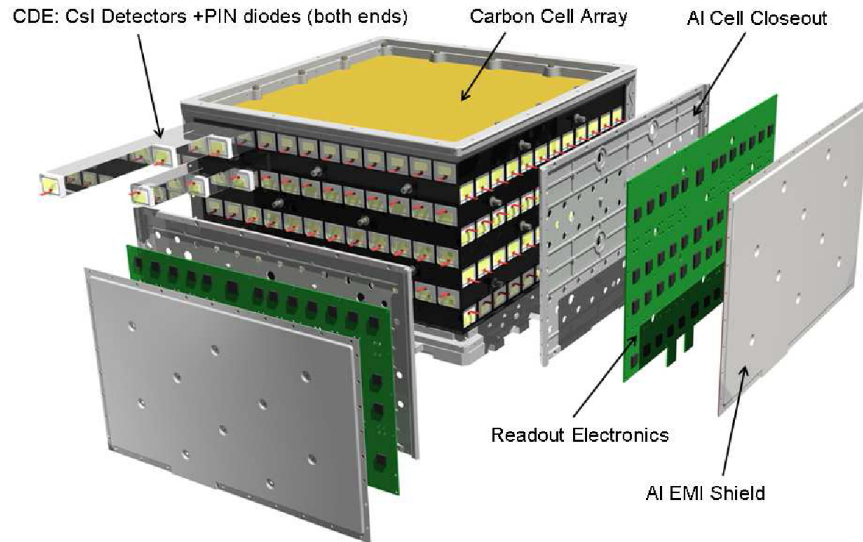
Un modulo del calorimetro. Da notare la struttura a 8 layers e la loro disposizione.
